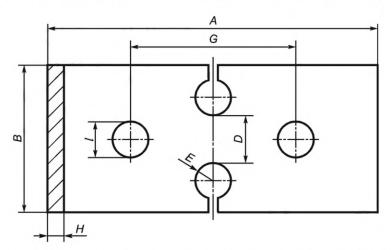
Образец для испытания типа A, полученный механической обработкой для испытания при растяжении (для e < 25 мм)
